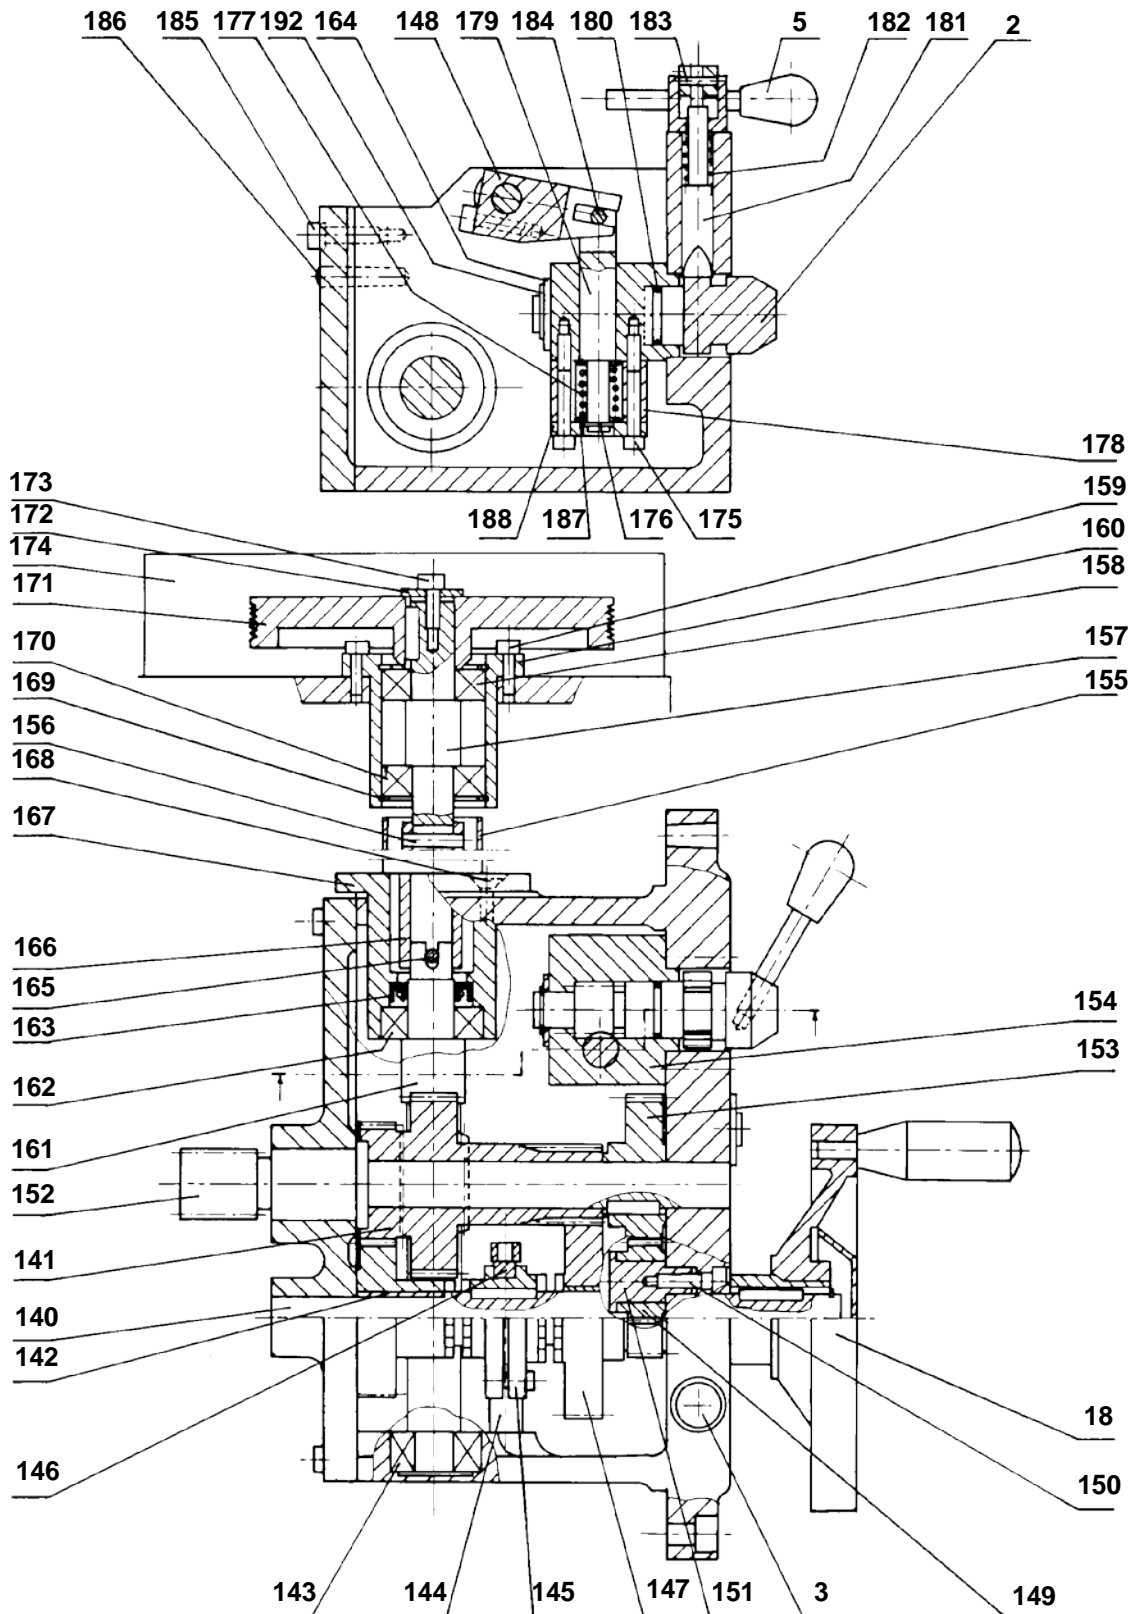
РЕДУКТОР ПОДАЮЩЕГО СТОЛА В РАЗРЕЗЕ
